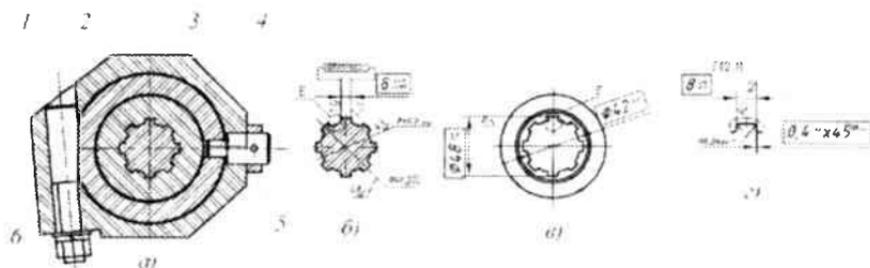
Схема расчета шлицевого соединения поворотной цапфы управляемого колеса: а, б, в, г – соответственно поперечное сечение поворотной цапфы управляемого колеса, выдвигного шкворня, шлицевой втулки и шлицы; 1 – кронштейн; 2 – обойма; 3 – шлицевая втулка; 4 – выдвигная шкворня; 5 – палец; 6 – клин
